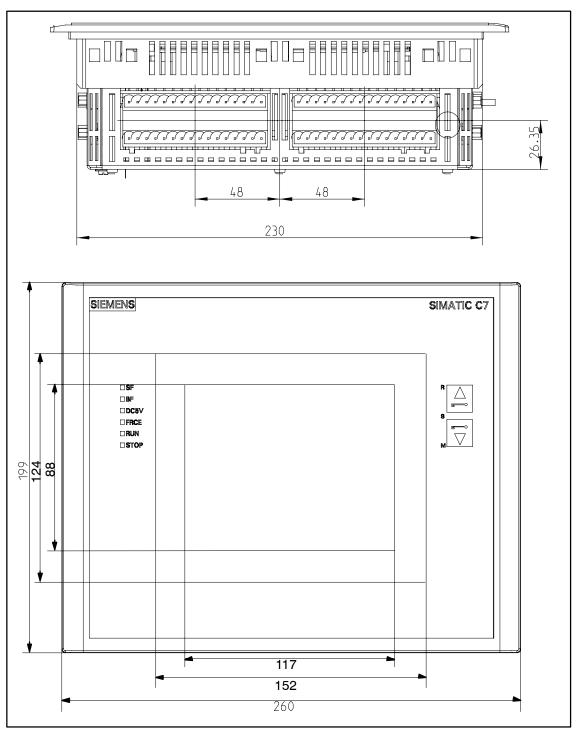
Maßbilder für das C7-635 Touch(Maße in Millimeter)
